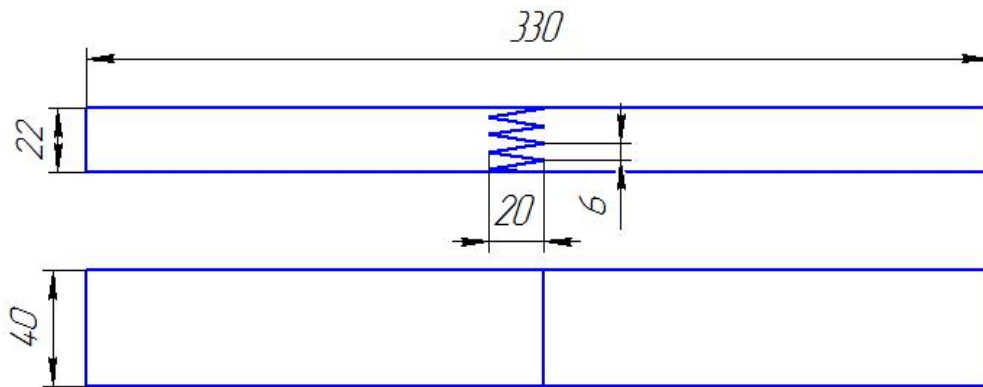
Конструкція зрізаної заготовки із ВЖД товщиною 22 мм
